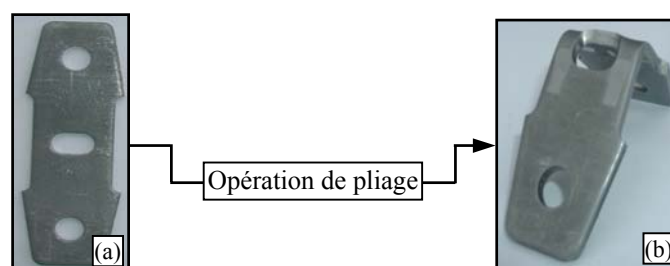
Etats initial (a) et final (b) des éprouvettes considérées
